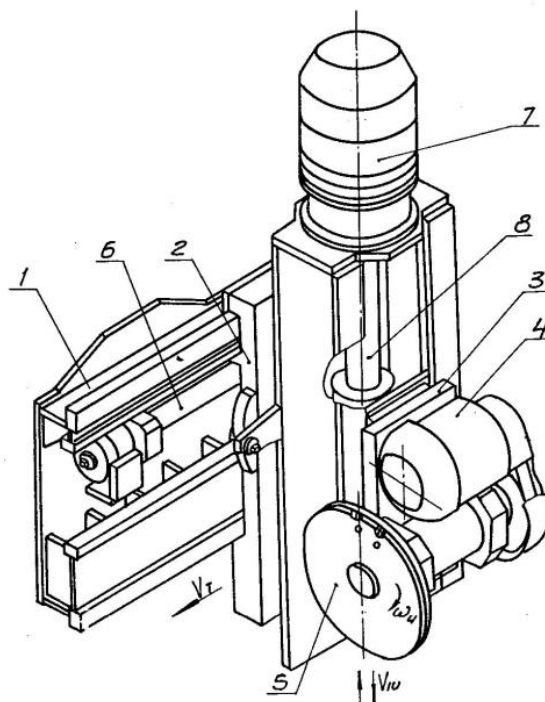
Принципова конструкція одношпindelного спеціального супорта до вертикально-зубофрезерного верстата мод. 5А342
